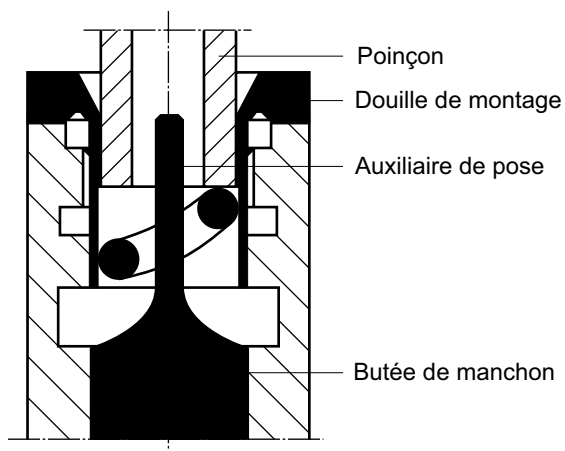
Le support de montage est complété par un manchon afin de protéger le joint des arêtes vives.
